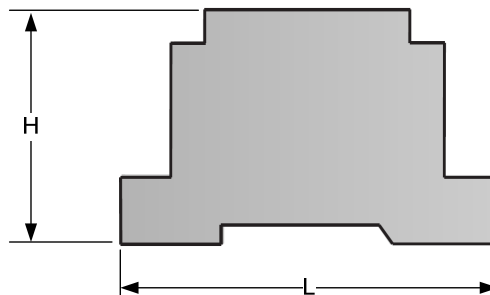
Dimensiones vista superior – Versión STX810-DIN
